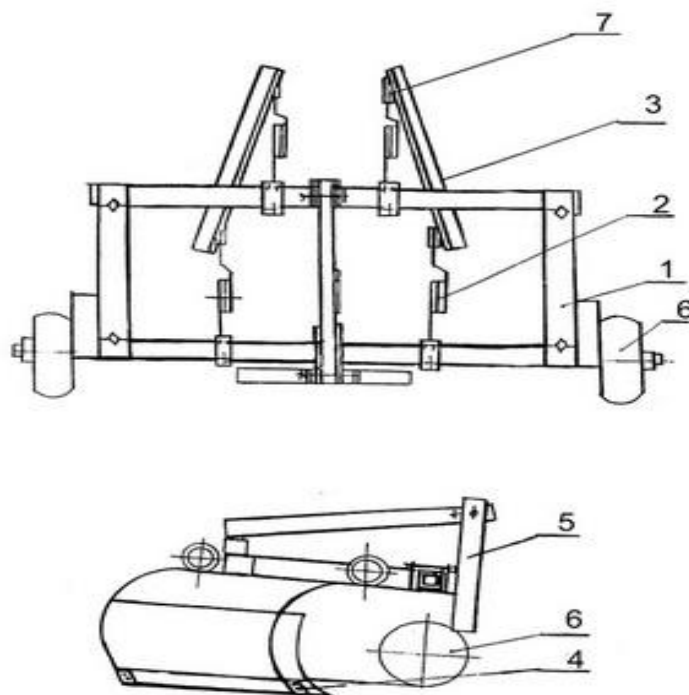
Комбинированный агрегат для рыхления и окучивания:
